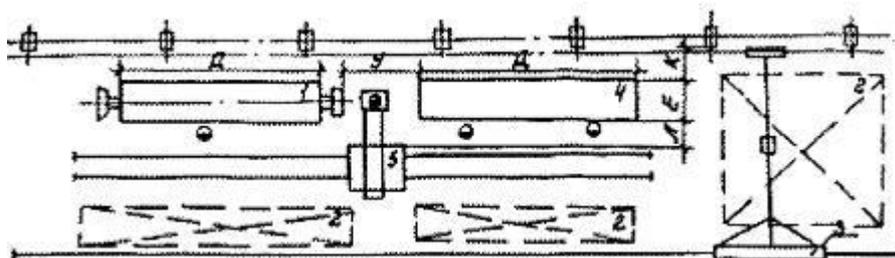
Размещение стенов, кантователей для сварки крупногабаритных сварных сборочных единиц
